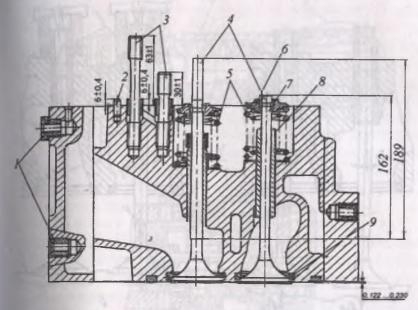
Головка блока цилиндров ЯМЗ-840
